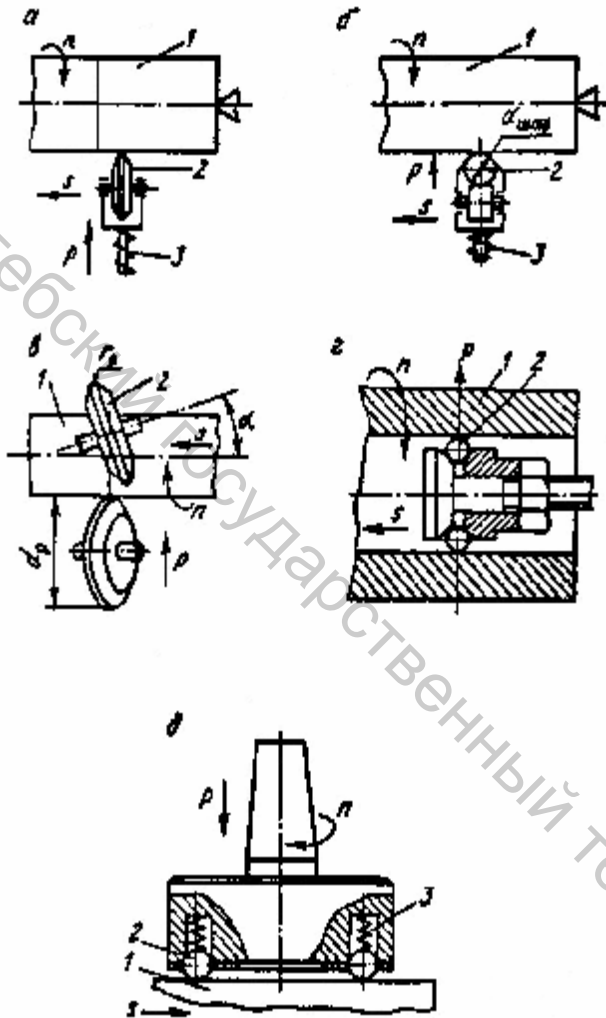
Схемы обработки способом ППД с качением инструментов: 1- заготовка, 2- инструмент; 3- пружина
